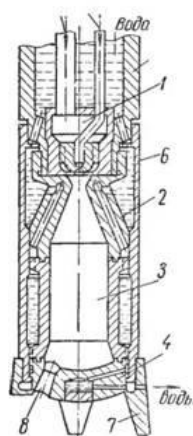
Схема трёхсопловой реактивной горелки: 1 – форсунка; 2 – корпус горелки; 3 – камера сгорания; 4 – головка горелки; 5 – переходник; 6 – кожух; 7 – башмак; 8 – сопло
